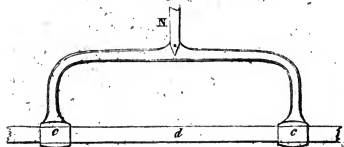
N extrémité du levier servant à manœuvrer la pompe; c c œil pratiqué à chaque extrémité de l'arc adapté au levier;
